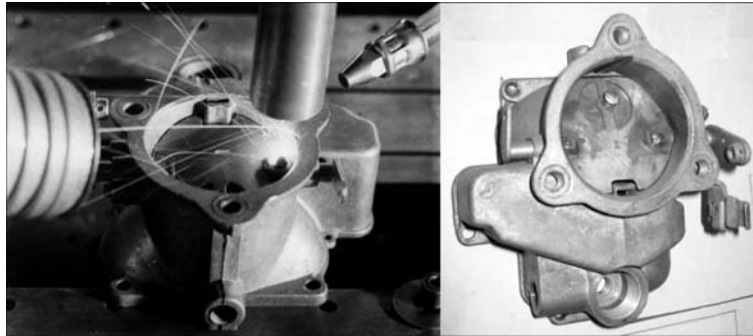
Лазерная сварка воздушной заслонки карбюратора (слева) и собранный с помощью лазерной сварки узел (справа)
